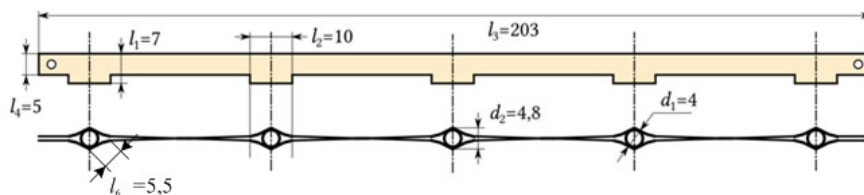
Чертеж контактной пластины 5-розеточного СФ
